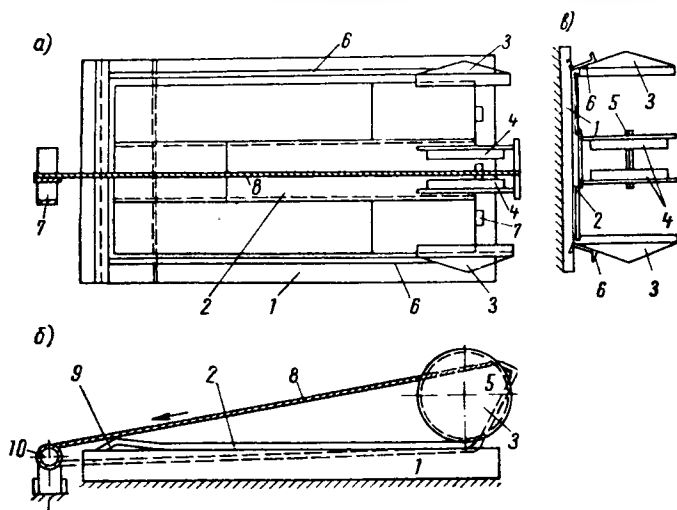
Сборка габаритного резервуара методом навертывания (Челябинский завод металлоконструкций им. С. Орджоникидзе)
